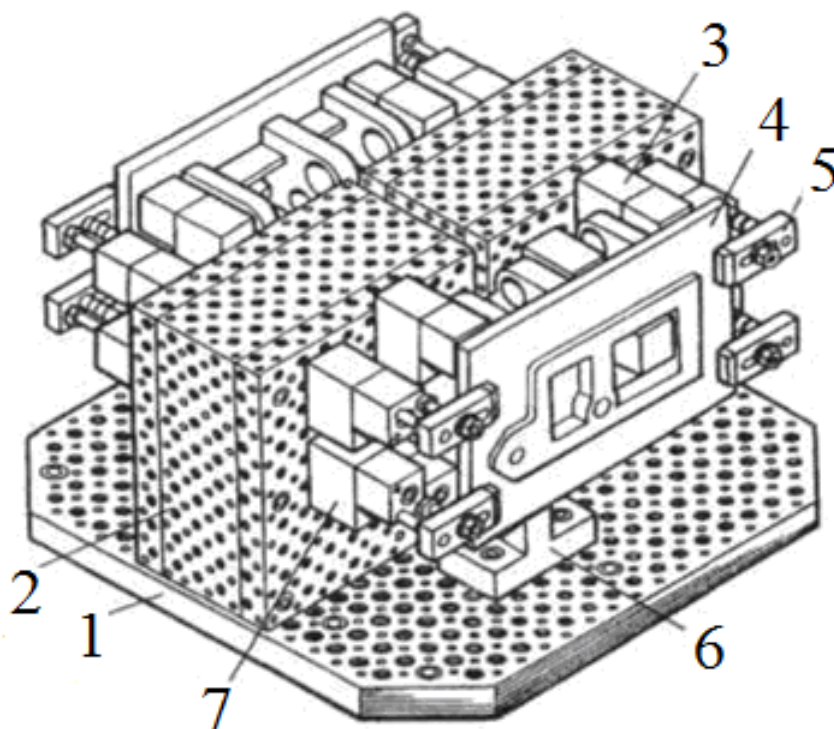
Двомісне верстатне пристосування для установлення корпусних деталей
